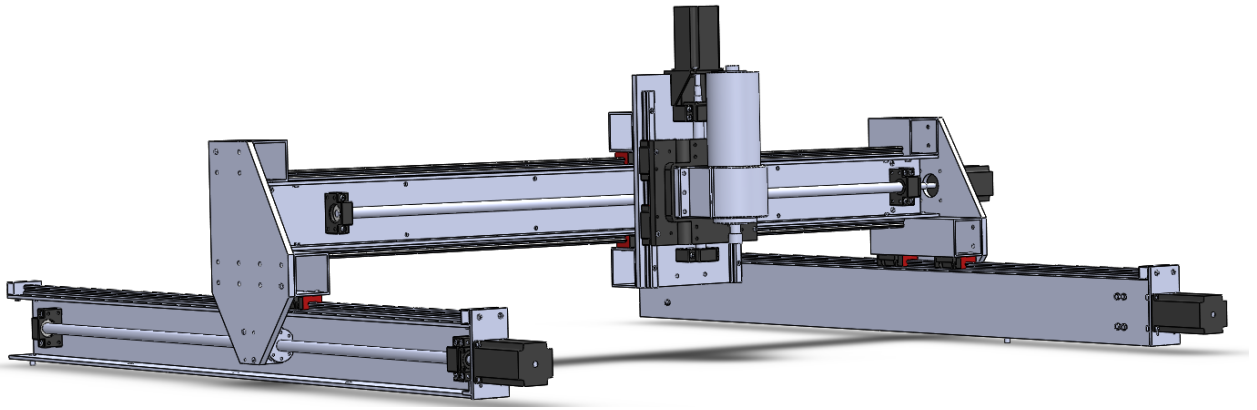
Змодельована верхня частина збірки (без столу) фрезерного верстату з ЧПК
